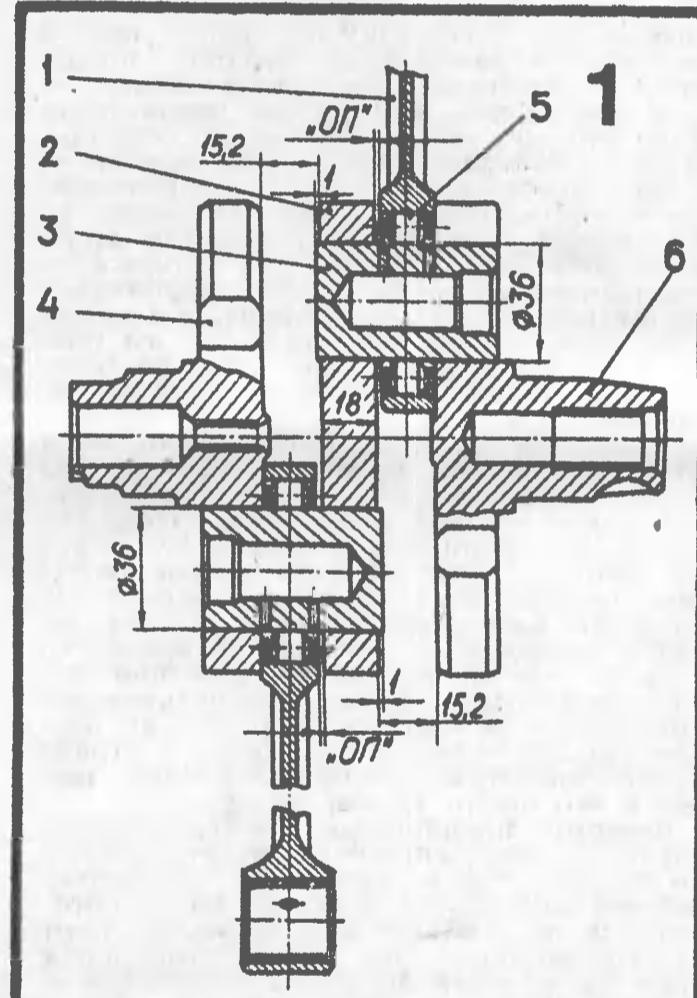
Коленчатый вал двигателя К-750М: 1 — шатун; 2 — щека кривошипа; 3 — палец; 4 — передняя цапфа; 5 — роликовый подшипник; 6 — задняя цапфа.
